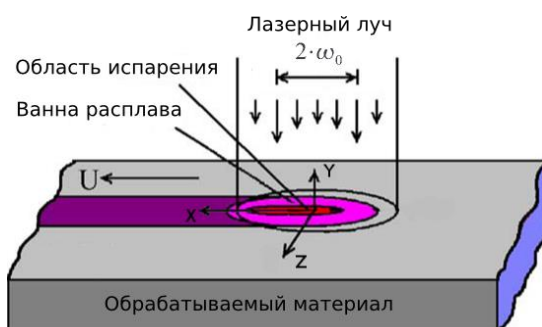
Схема процесса лазерной поверхностной обработки
